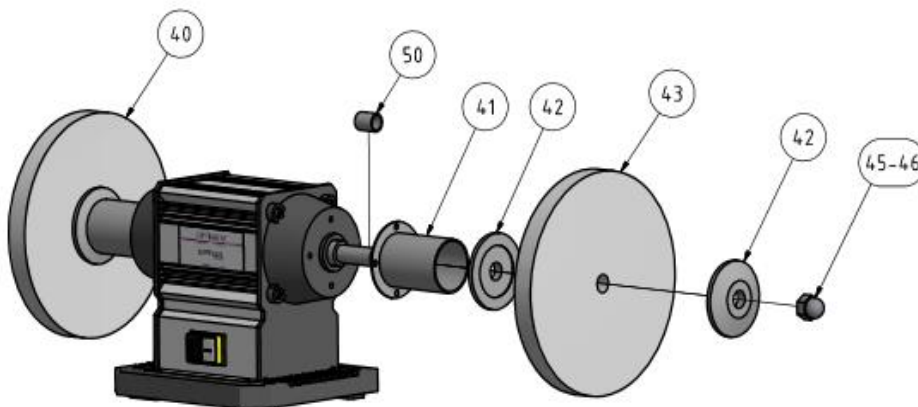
Ersatzteilzeichnung - Spare parts drawing
